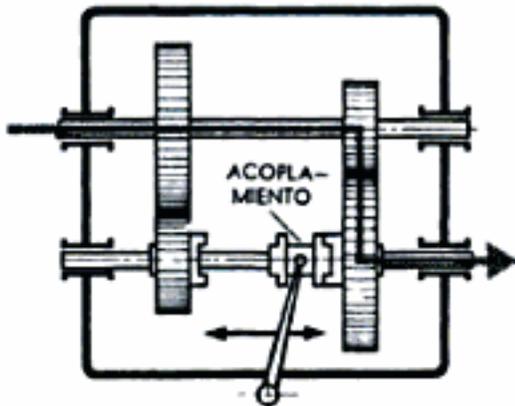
,1 Mecanismo de engranajes con acoplamiento
